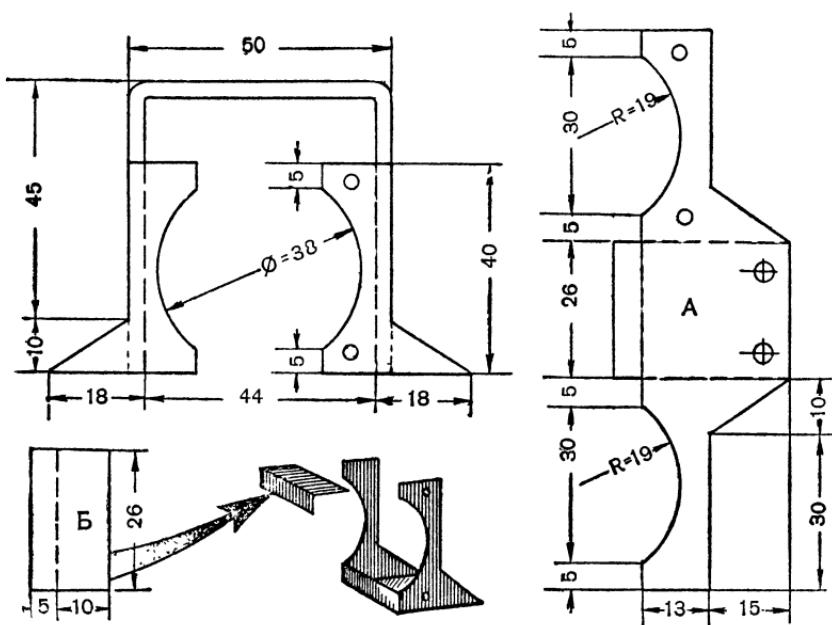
Детали статора № 10 (рис. 36): А — заготовка для башмака;
